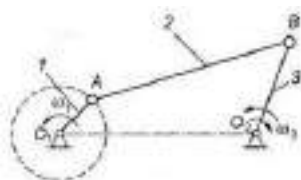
Шарнирный четырехзвенный механизм: 1 — кривошип; 2 — шатун; 3 — коромысло
